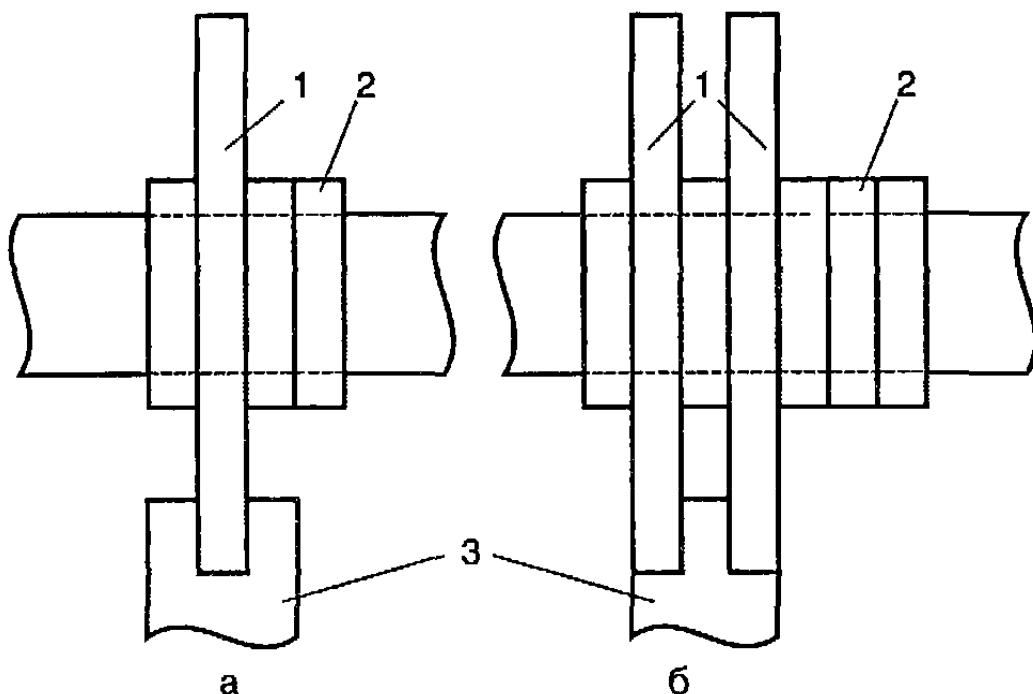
Схема изготовления вагонки двумя (тремя) пазовыми фрезами:
